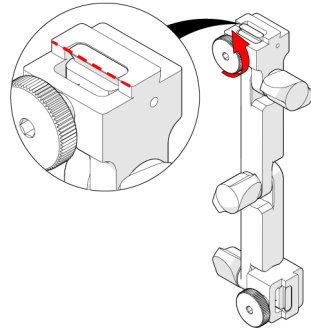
Desserrer la vis à ailettes du support de la caméra
